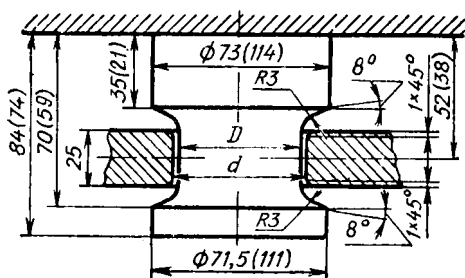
Номинальные размеры сцепного шкворня, захватов и отверстия разъемно-сцепного механизма по ГОСТ 12017—74 (размеры в скобках — для полуприцепов массой свыше 40 т)
